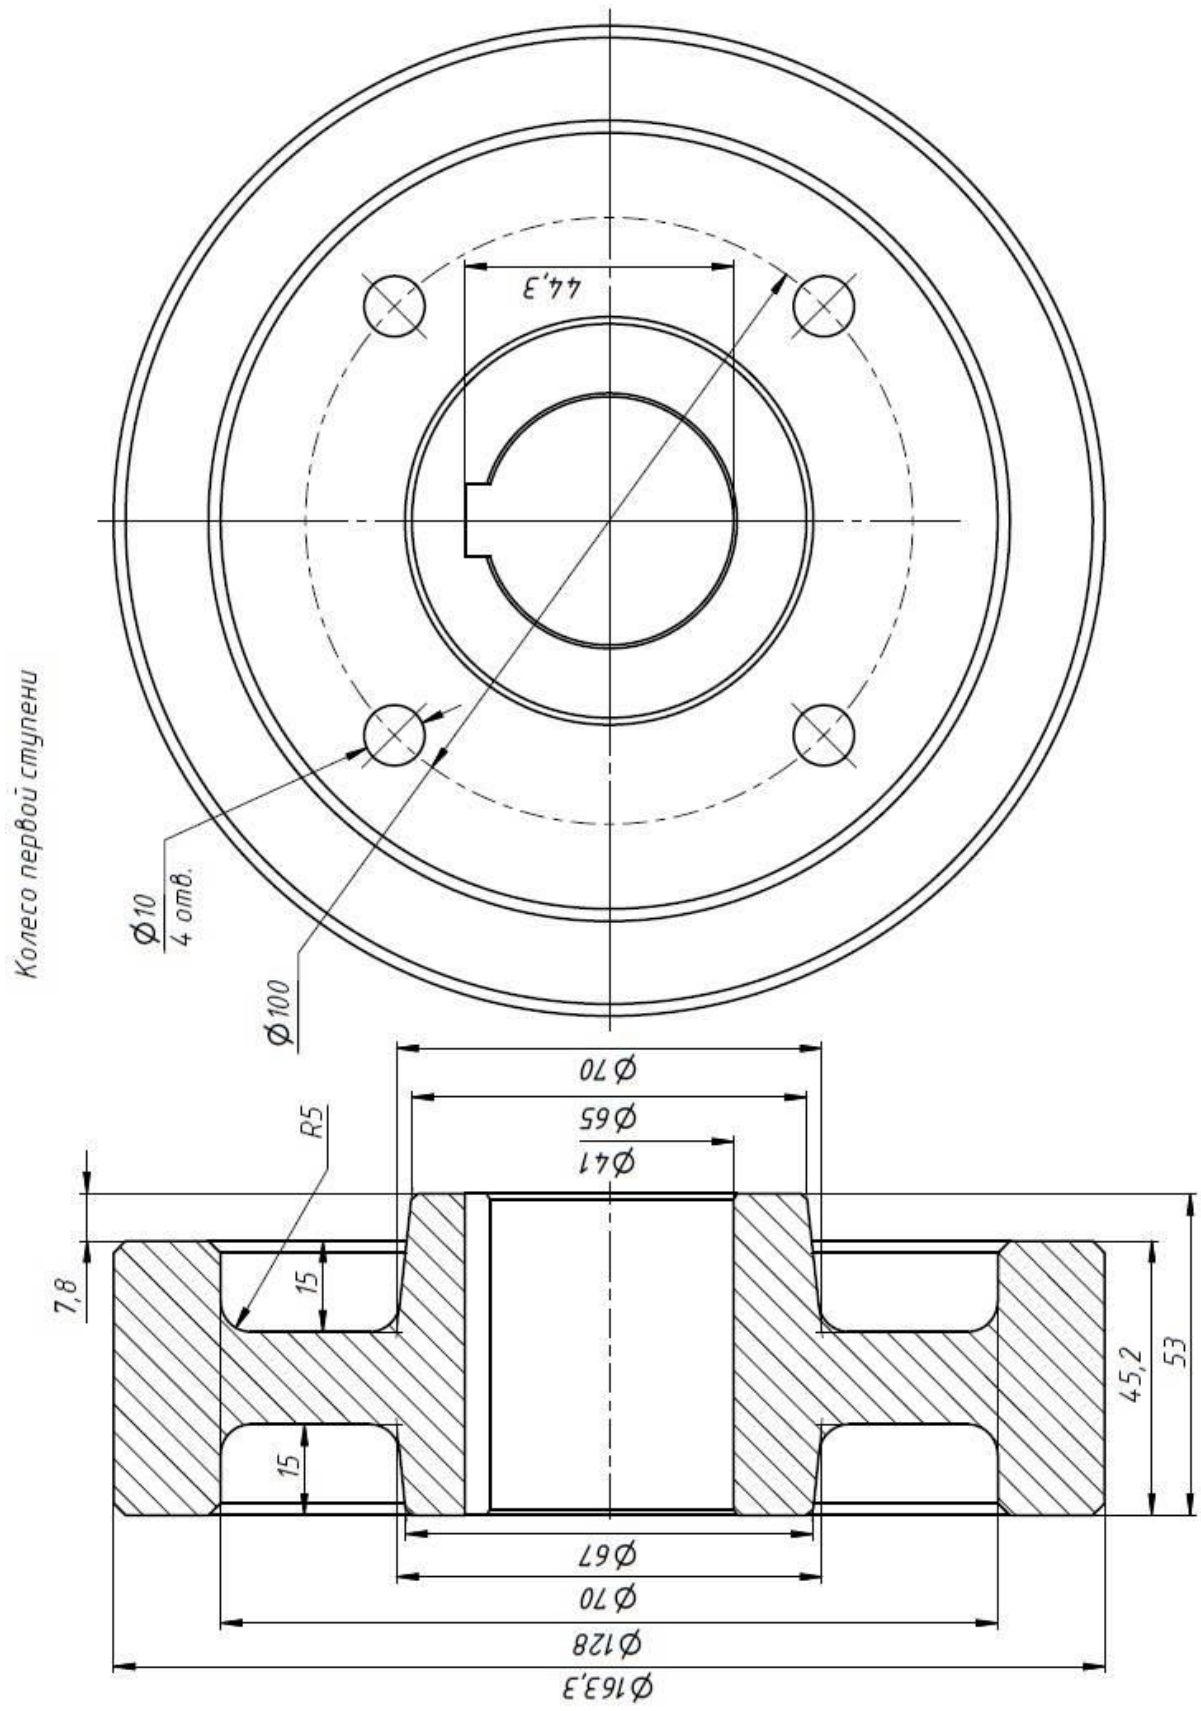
Чертеж колеса первой ступени редуктора с эвольвентным зубчатым зацеплением
